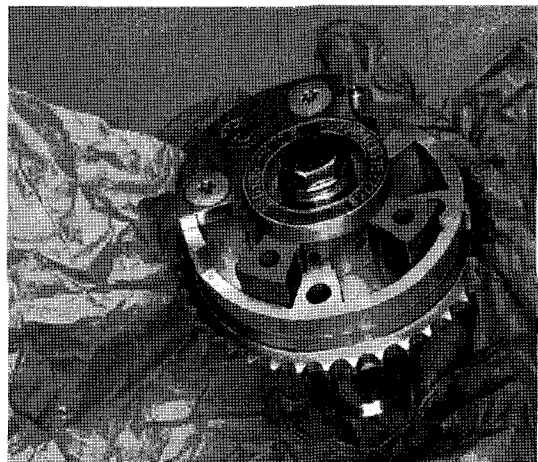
과공정 Al-Si 합금분말소재의 Chain Sprocket이 내장된 BMW社의 Camphaser System⁷⁾.
